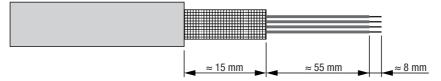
Confección del cable para el módulo de bornes MK 308
